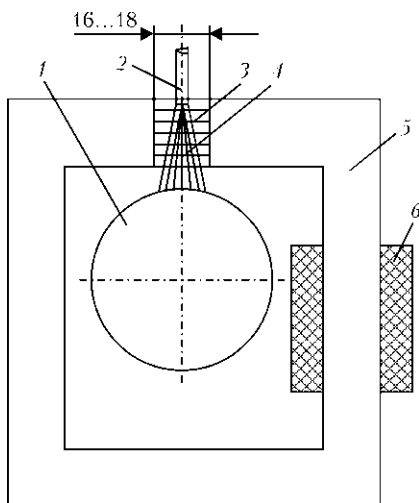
Схема УВ ПОМП в зону горения сварочной дуги [12]: 1 — наплавляемый образец; 2 — электродная проволока; 3 — магнитные силовые линии; 4 — столб сварочной дуги; 5 — сердечник электромагнита; 6 — катушка
